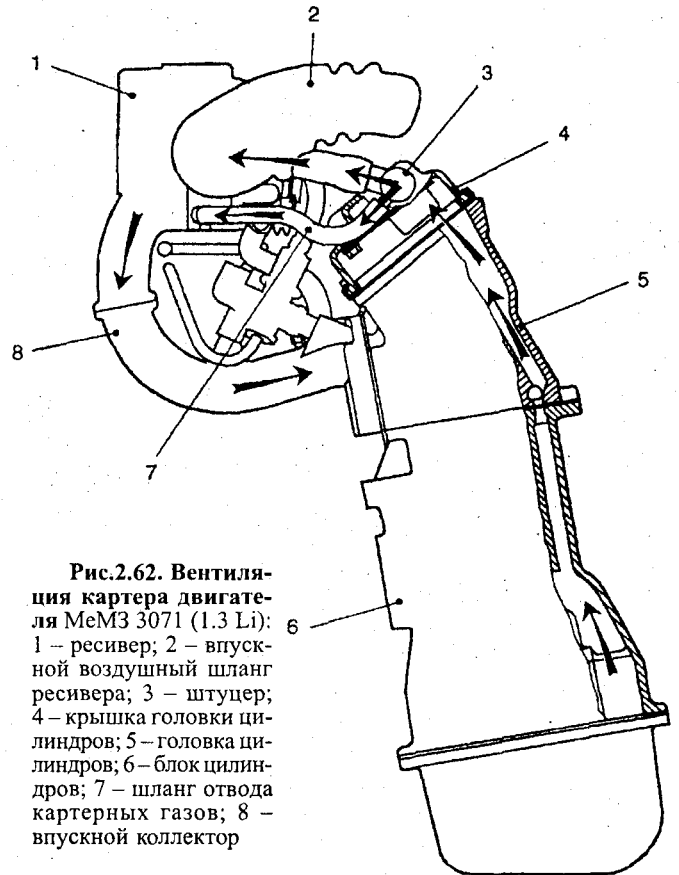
Вентиляция картера двигателя MeMZ 3071 (1.3 Li): 1 – ресивер; 2 – впускной воздушный шланг ресивера; 3 – штуцер; 4 – крышка головки цилиндров; 5 – головка цилиндра; 6 – блок цилиндров; 7 – шланг отвода картерных газов; 8 – впускной коллектор
